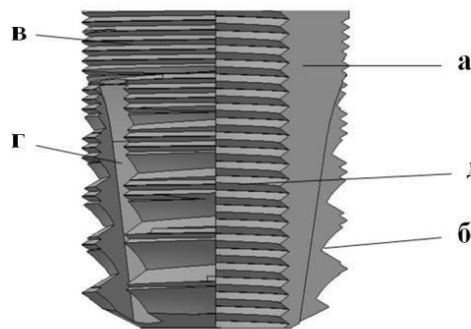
Дентальный имплантат-имитатор конструкции автора: а - имплантат-имитатор в разрезе; б - крупная резьба; в - мелкая резьба; г - ассиметричные пазы; д - внутренняя резьба для костного трепана, элеватора и штуцера
